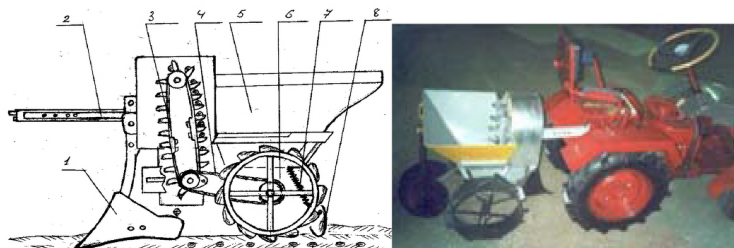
Технологическая схема картофелепосадочной машины: 1 – сошник; 2 - прицепное устройство; 3 - цепочно-ложечковый высаживающий аппарат; 4 - механизм привода высаживающего аппарата; 5 - бункер для клубней; 6 - два опорно-приводных колеса; 7 - пружина со штангой; 8 - бороздозакрывающие диски.
